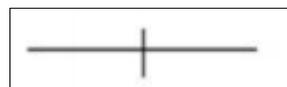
Simbología unión soldada.
